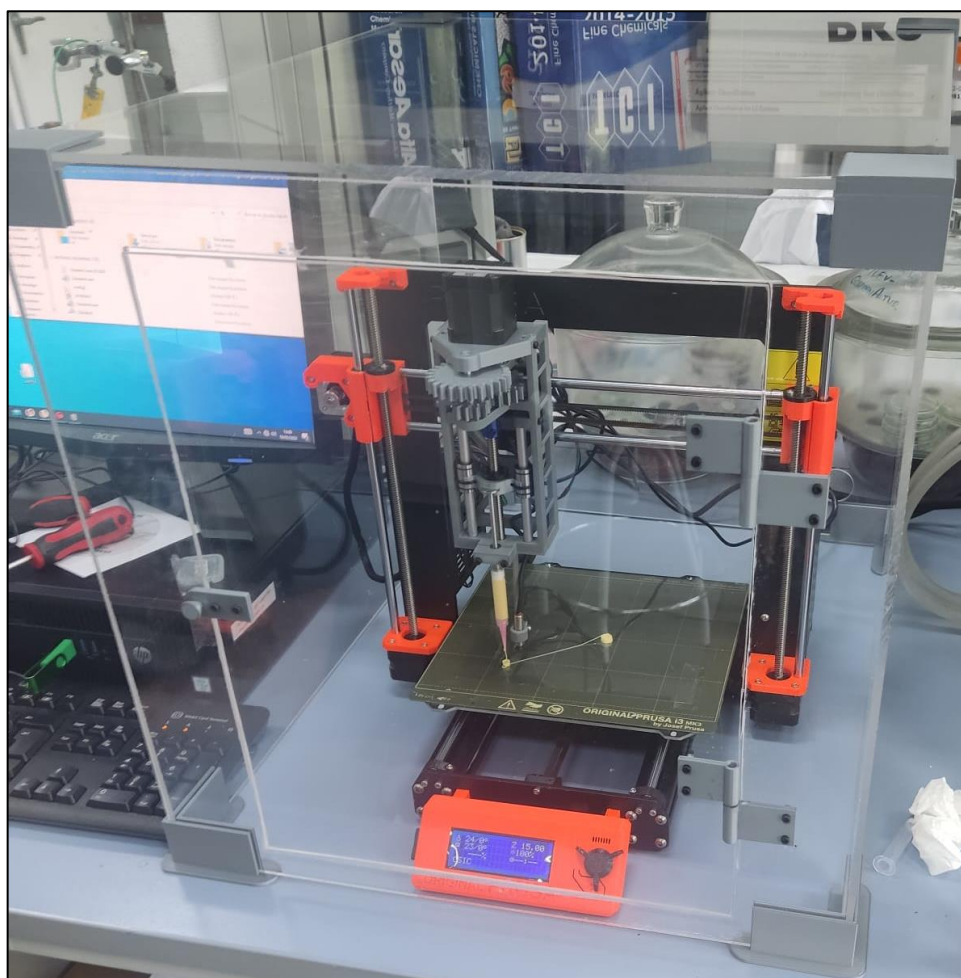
Impresora Prusa MK3S+ adaptada para la impresión de pastas.
